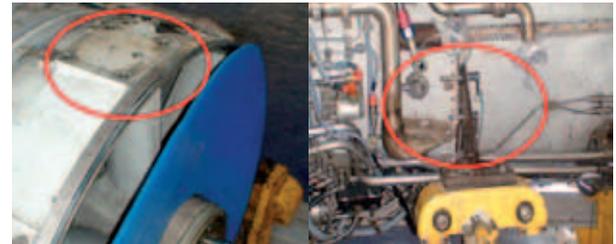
Banco a modificar del motor ATAR 09C-5, el cual también posee mecanismos para hacerlo rotar, tiene que ser adaptado para el motor J-79JIE
